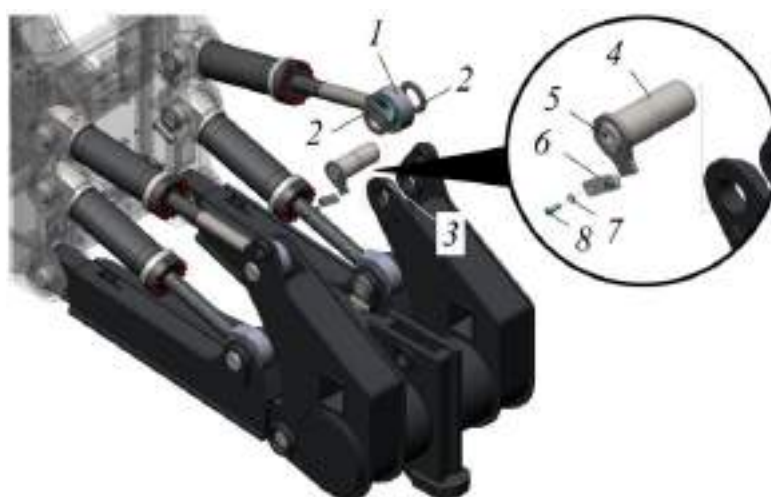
Соединение балки с верхнем гидроцилиндром
